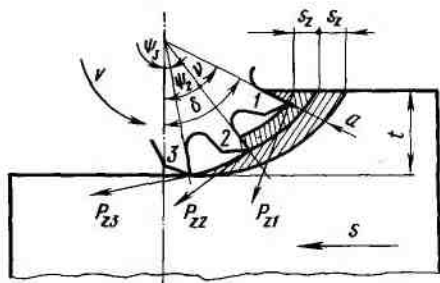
Суммарная площадь поперечного сечения среза при фрезеровании цилиндрической фрезой
